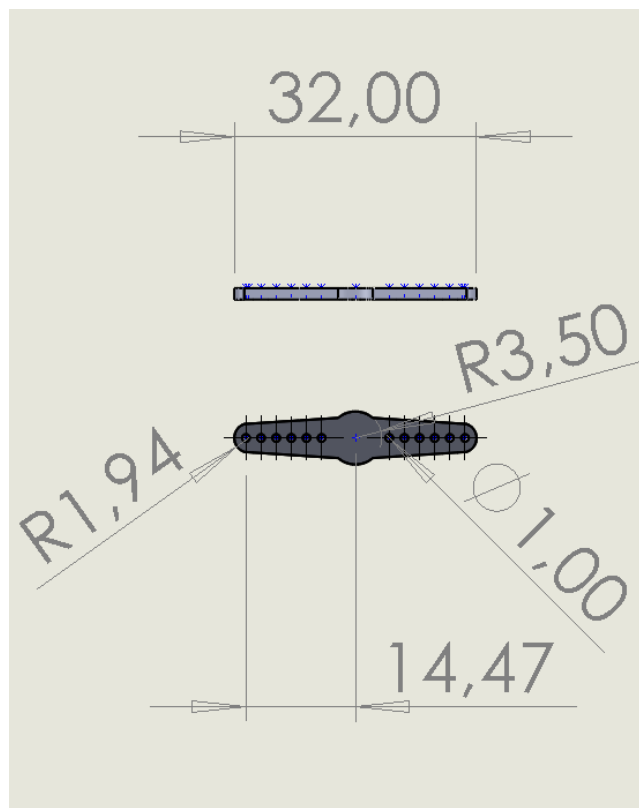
Dimensiones aleta doble que se conecta a la parte de giro del motor.
